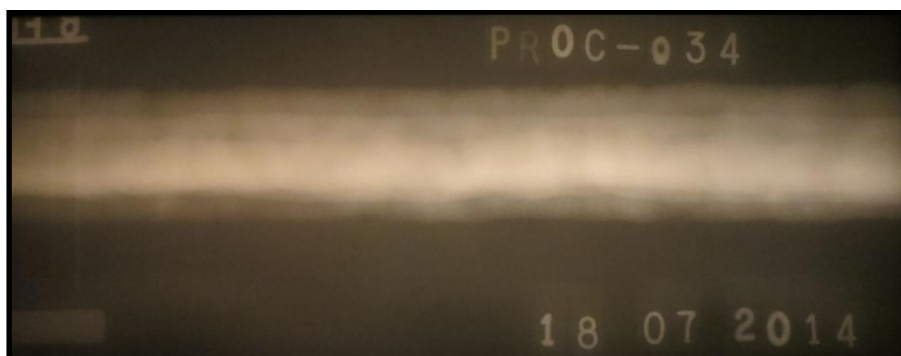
Radiografia - Soldadura realizada com fio FABSHIELD XLR-8.
